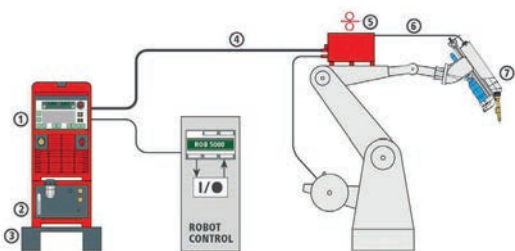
Процес лазерно-гібридного зварювання зі зварювальною головкою LaserHybrid Twin
